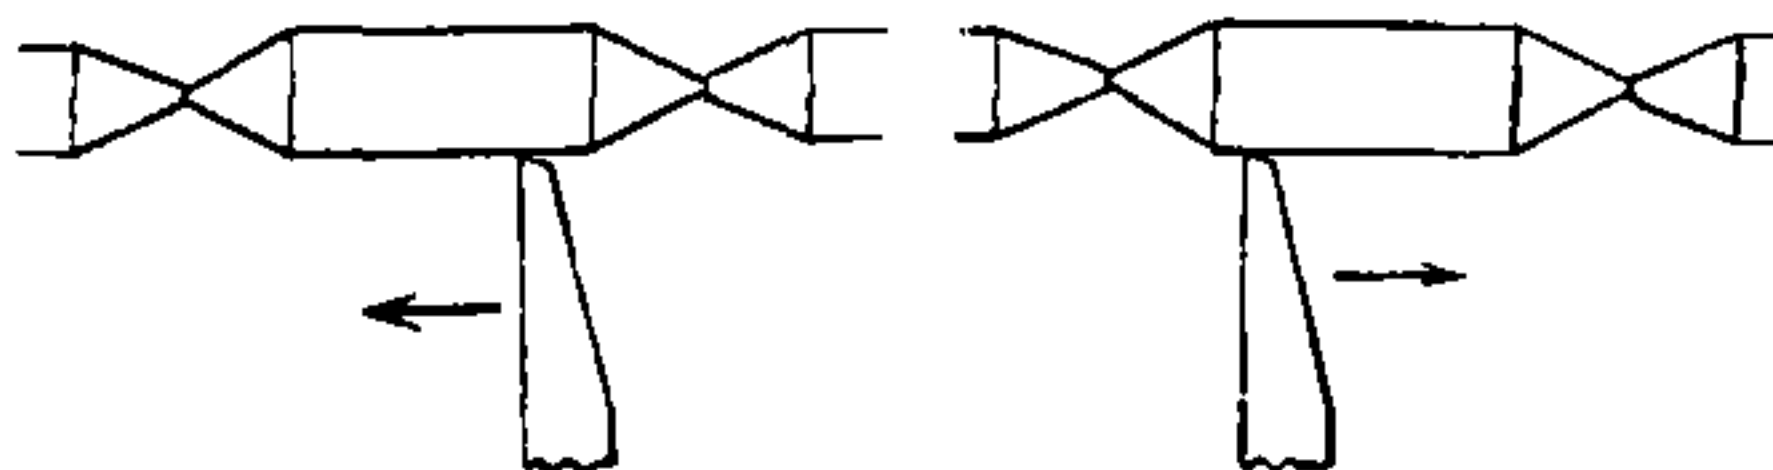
La direzione del movimento dell'utensile di tornitura è molto importante.
